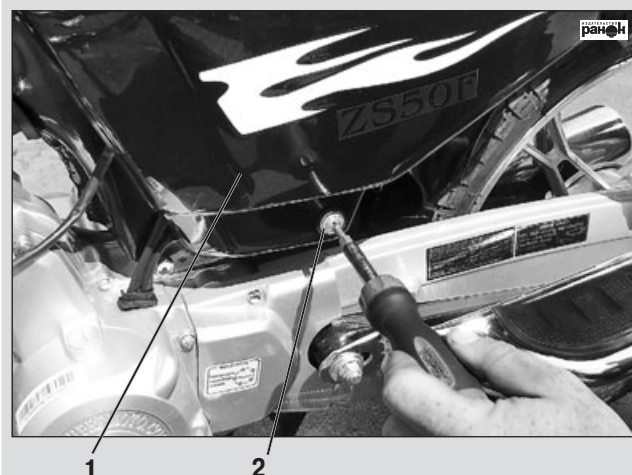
Снятие крышки облицовки мотоцикла: 1 – левая крышка облицовки; 2 – винт крепления облицовки
